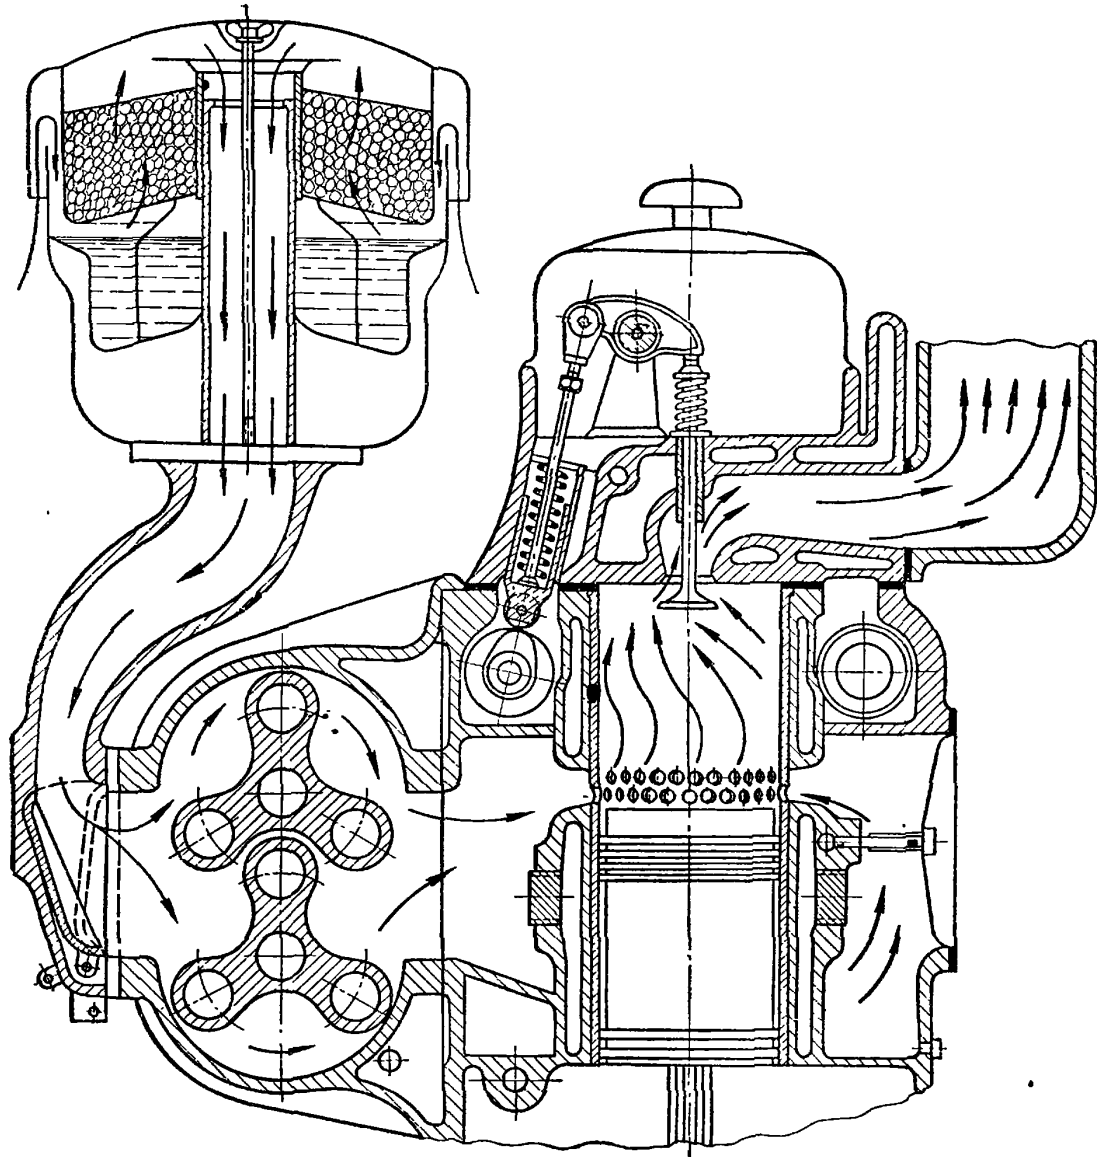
Поперечный разрез двигателя ЯАЗ-204
